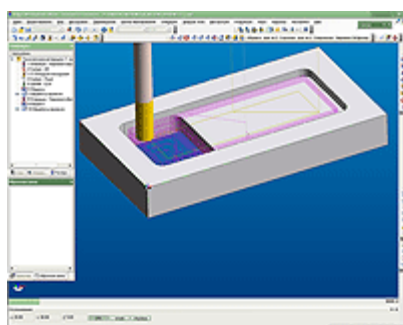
Edgescam. После выбора заготовки перейти в режим обработки и обработать детали.
